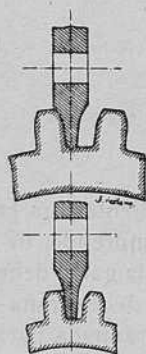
Construcción de engranajes cónicos en la fresadora universal.
